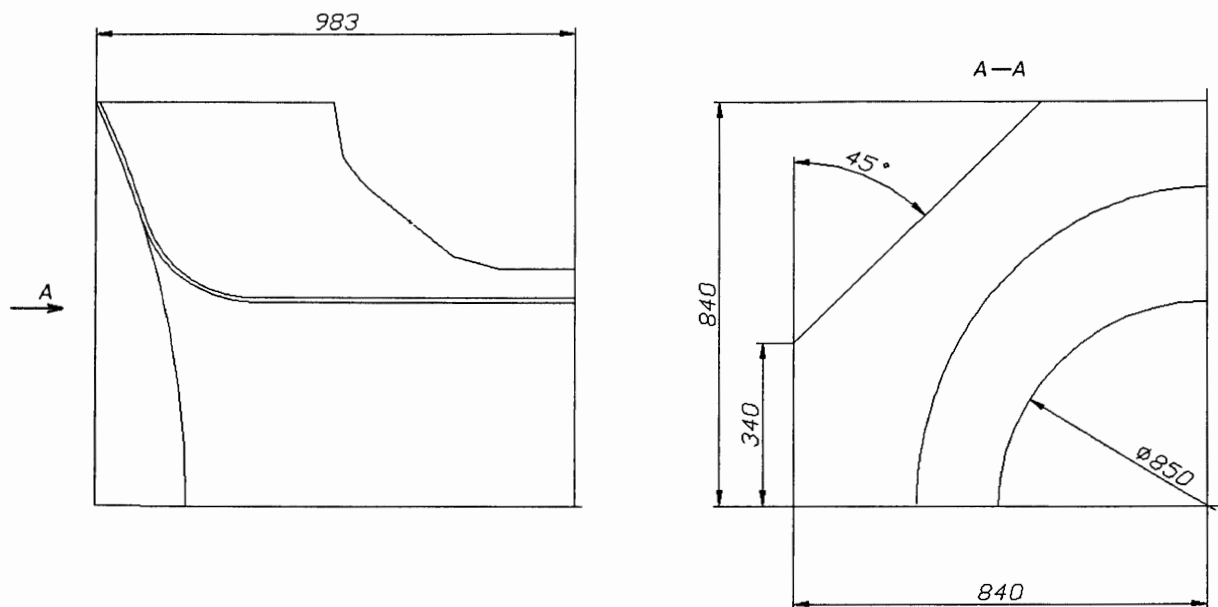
Испытательный образец патрубка ДN 850
